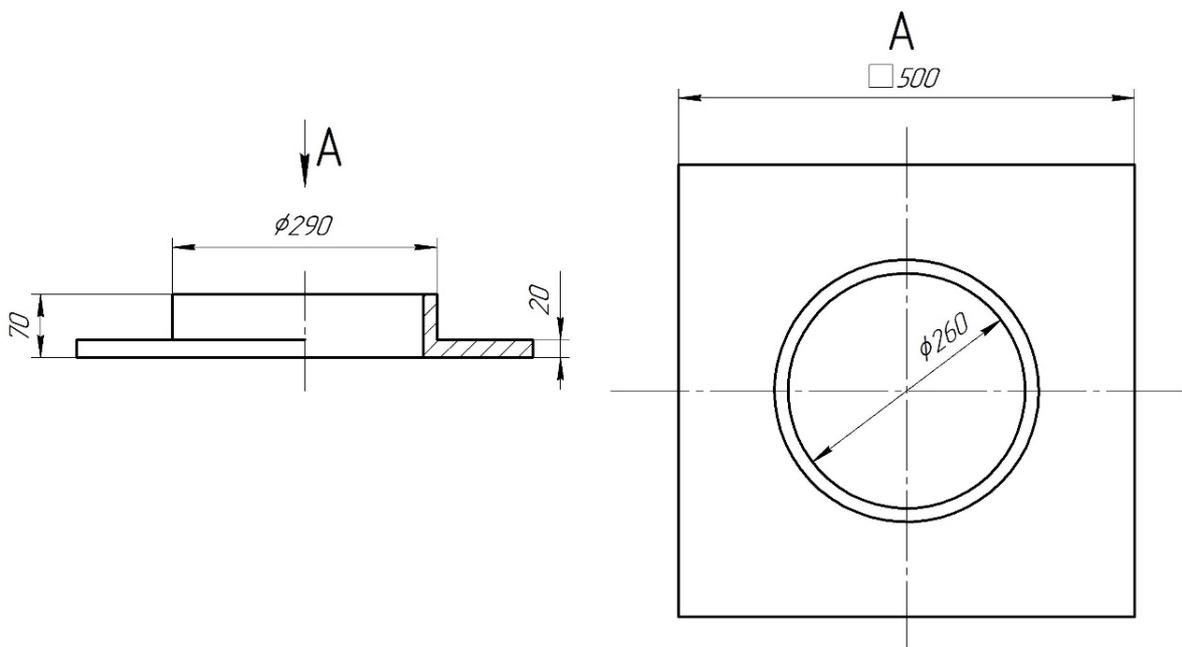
Чертеж верхней пластины корпуса ОПУ
